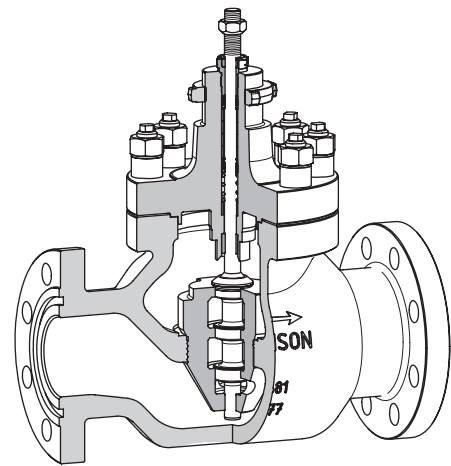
· Durchgangsventil Typ 3251 mit AC-3 Garnitur
